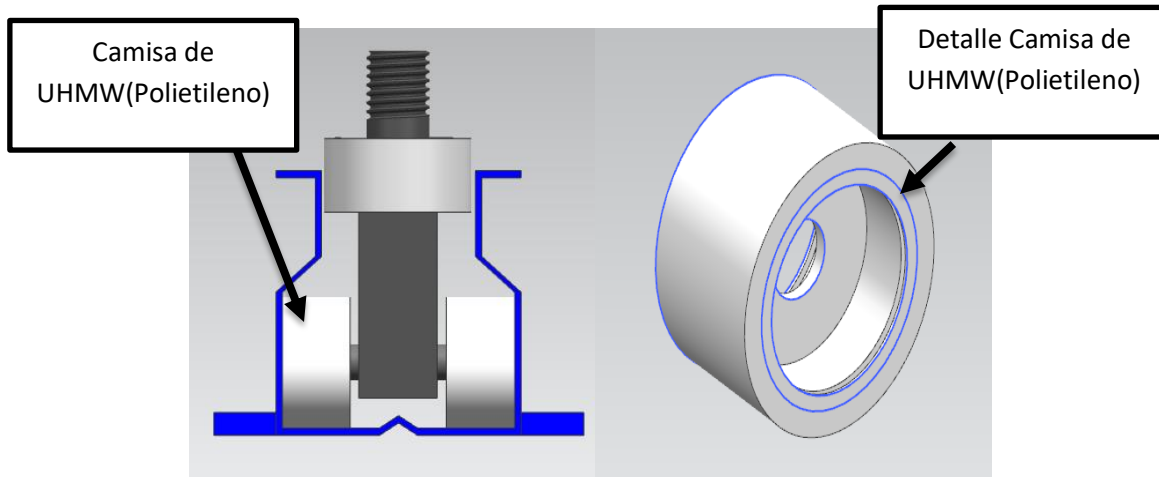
Detalle camisa de Polietileno. Fuente Propia
